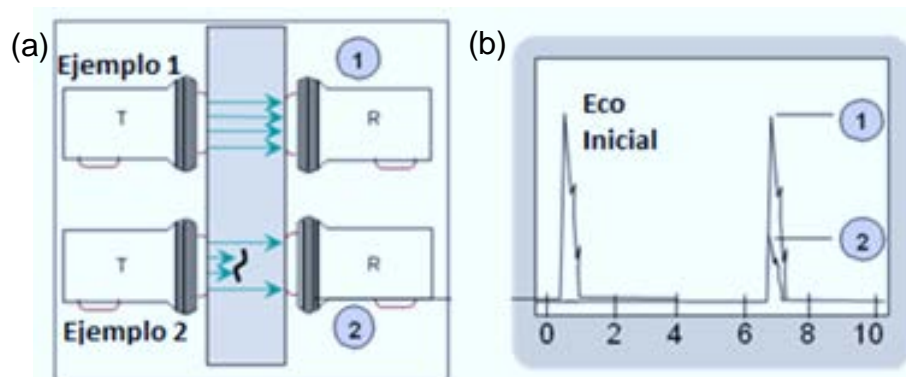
Método de transmisión: (a) Transductor emisor y receptor en una pieza sin defecto y con defecto interno; y (b) eco inicial y eco final sin defecto y eco final con defecto en la pieza analizada.
